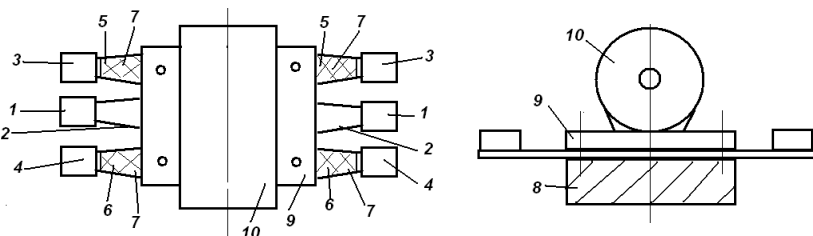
Багатомасовий ДГК, приєднаний до платформи обертової машини: а – вид зверху; б – вид збоку
